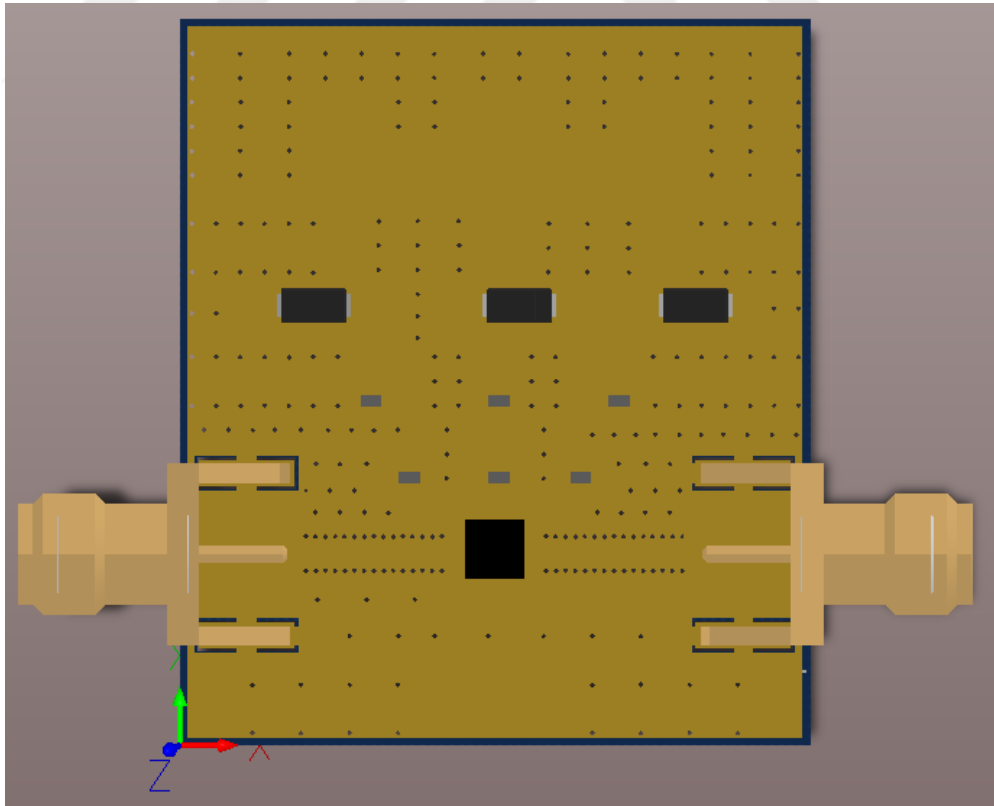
'de ise 3 boyutlu PCB devresi verilmiştir.
